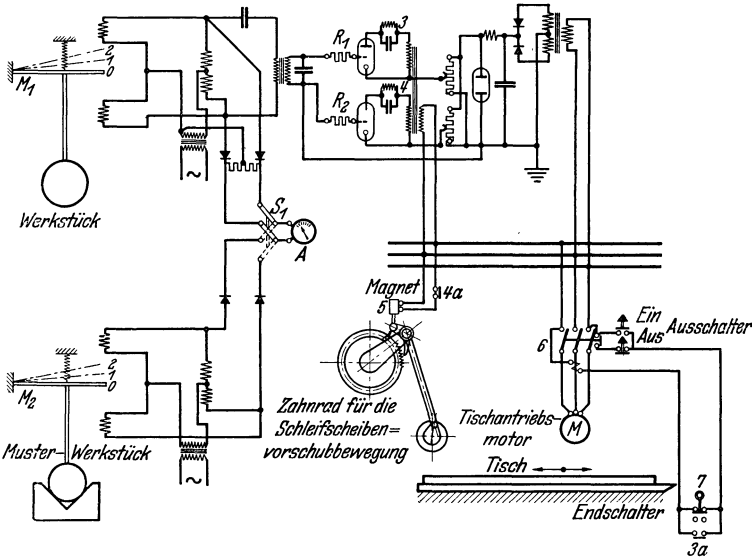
Selbsttätige Meßvorrichtung an einer Schleifmaschine.
